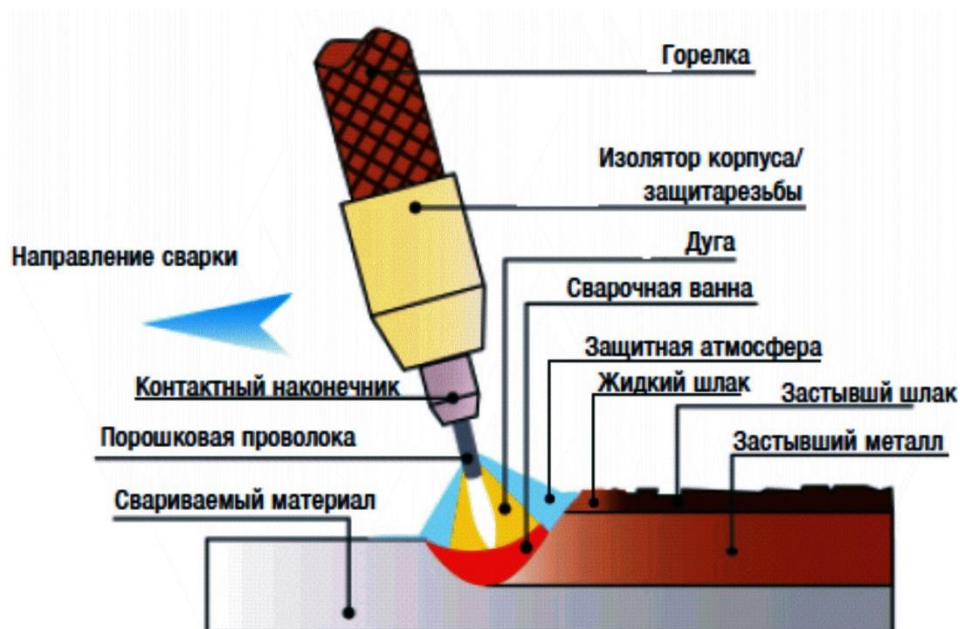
Схема процесса сварки самозащитной порошковой проволокой
